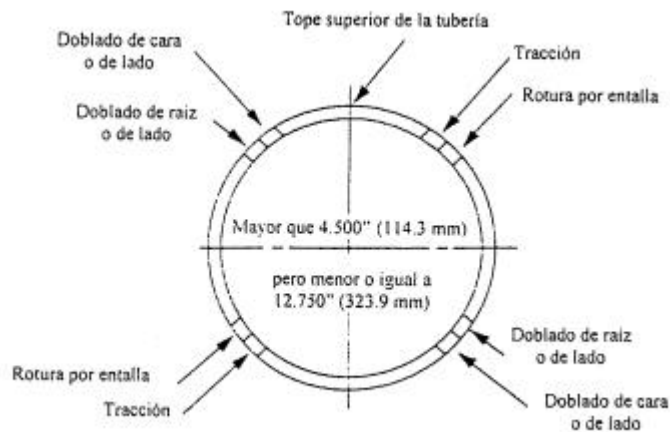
A: Ubicación de las probetas de ensayo de soldaduras a tope para ensayos de calificación de soldadores (mayor que 4.5" (114.3 mm))
